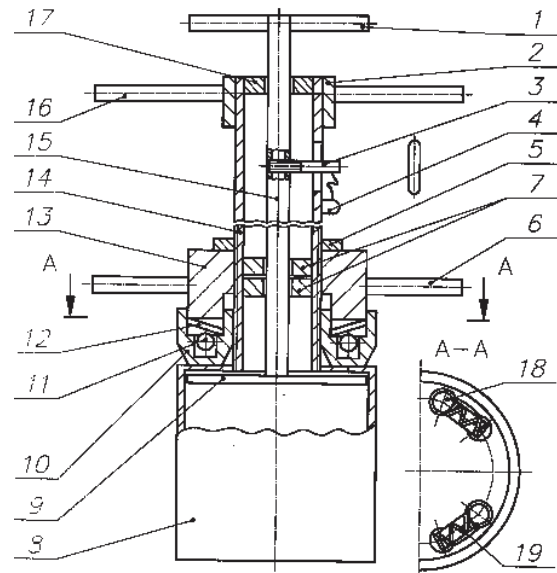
Устройство для вырезания образца почвы: 1 — ручка выталкивателя; 2 — муфта; 3 — поводок; 4 — выключатель концевой; 5 — контргайка (ГОСТ 8961-75); 6 — упор нижний; 7 — втулка направляющая; 8 — нож цилиндрический; 9 — выталкиватель; 10 — корпус; 11 — шарик; 12 — пружина дисковая; 13 — муфта; 14 — труба (3/4"); 15 — труба (8–10); 16 — упор верхний; 17 — втулка направляющая; 18 — шарик; 19 — пружина
